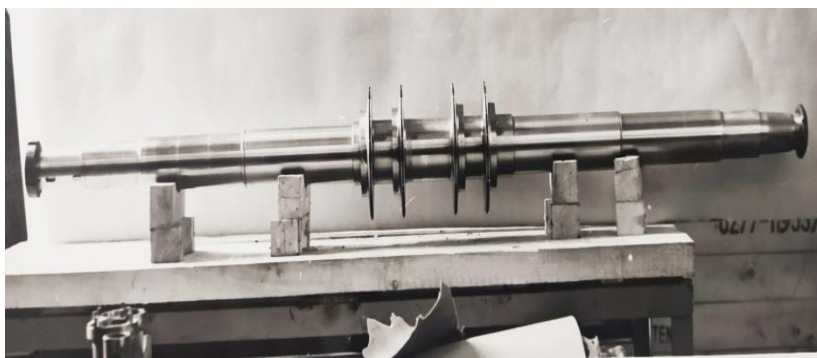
Ротор із робочими колесами виготовлений із суцільної заготовки
